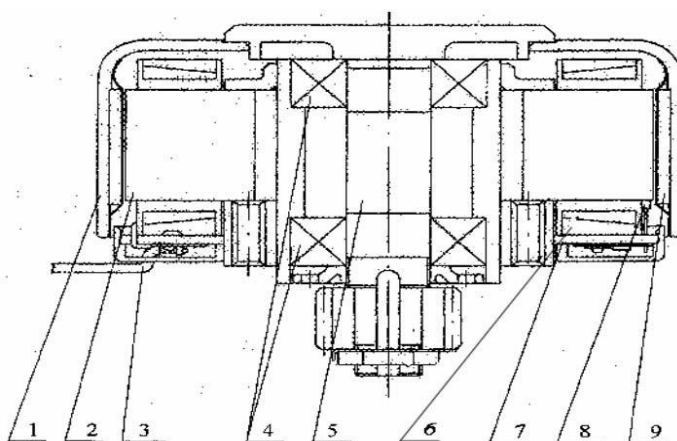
Сборочный чертеж вентильного двигателя
